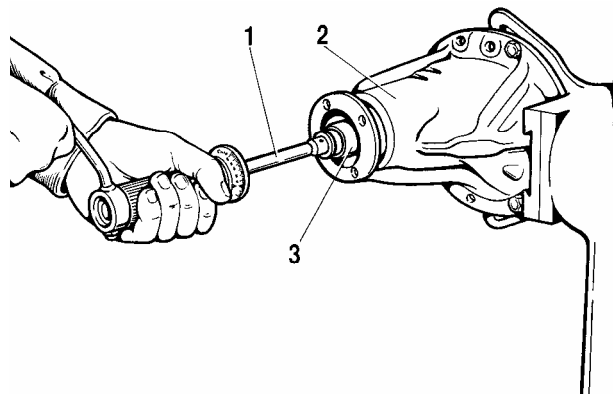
Проверка предварительного натяга подшипников ведущей шестерни:
